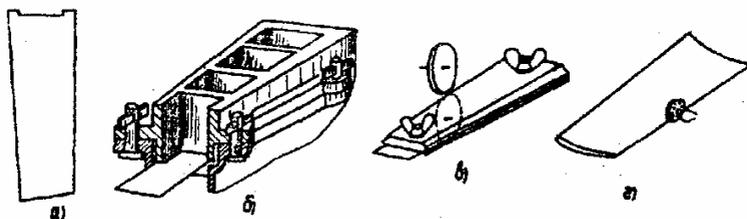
Изготовление пустотелой беззамковой спрямляющей лопатки:
